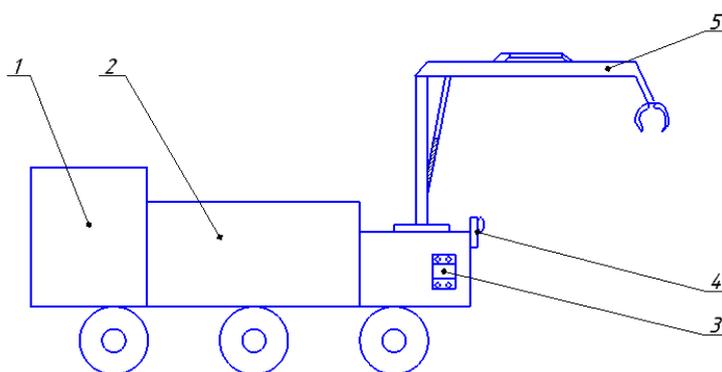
Основные части конструкции робота: 1 – блок управления и емкость для аккумуляторов; 2 – кузов для сбора образцов; 3 – камера для наблюдения положения руки; 4 – газоанализатор; 5 – рука для сбора образцов
